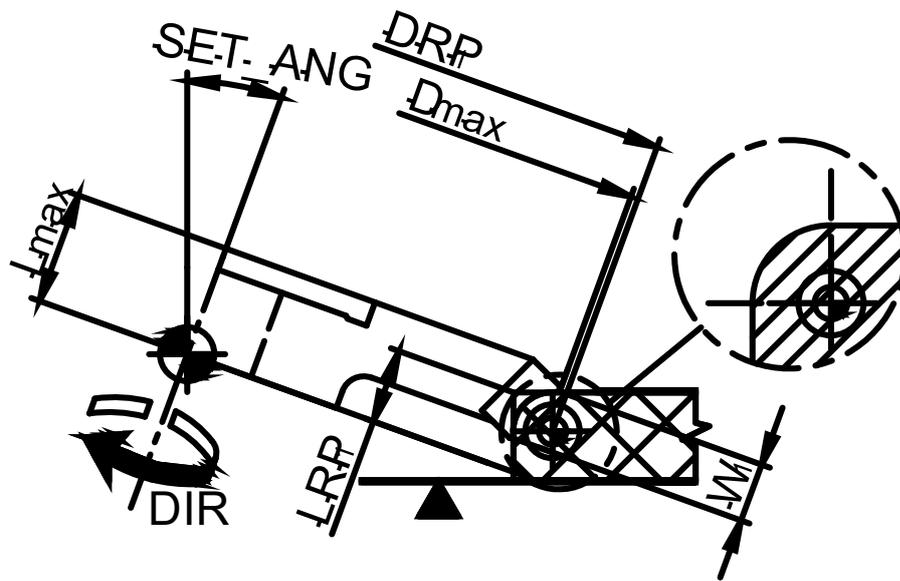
Maßdefinition für Postforming-Werkzeuge (Beispiel Abplatt- und Radiusfräser)
